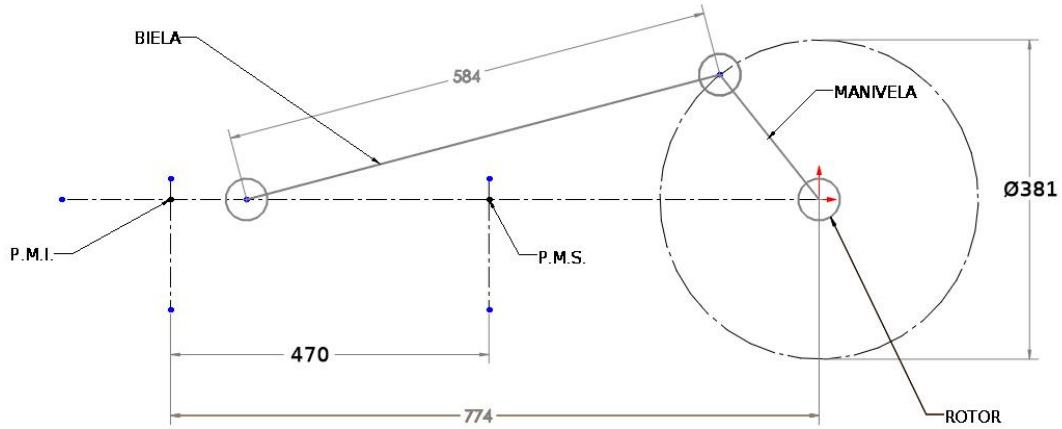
Esquema de la vista de planta del mecanismo (Dimensiones en milímetros).
